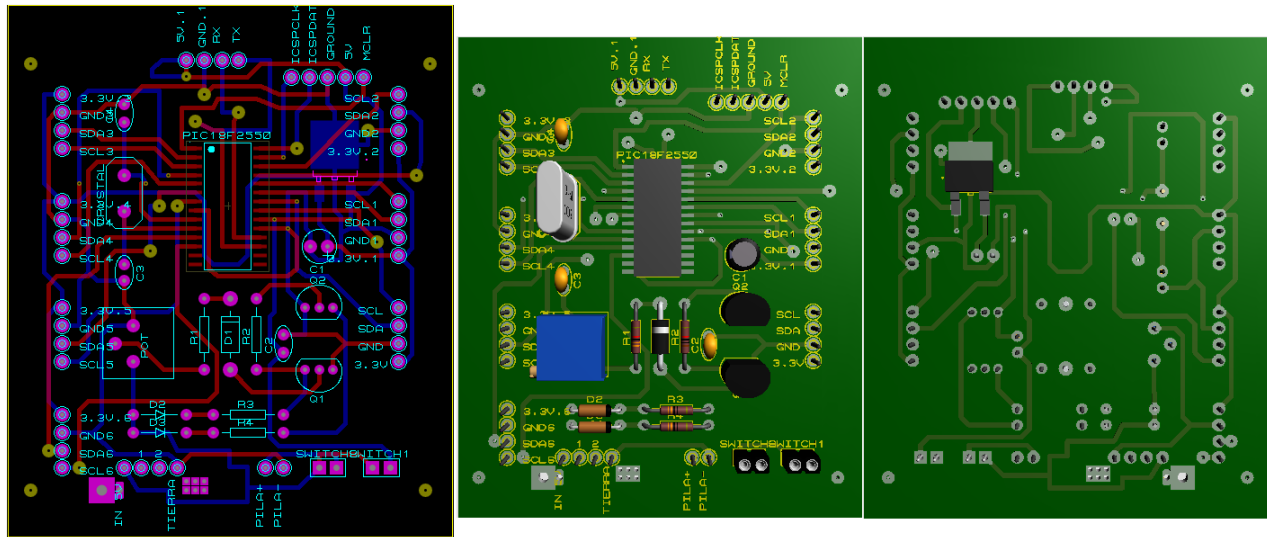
Diseño del PCB del prototipo final en Proteus ARES.
